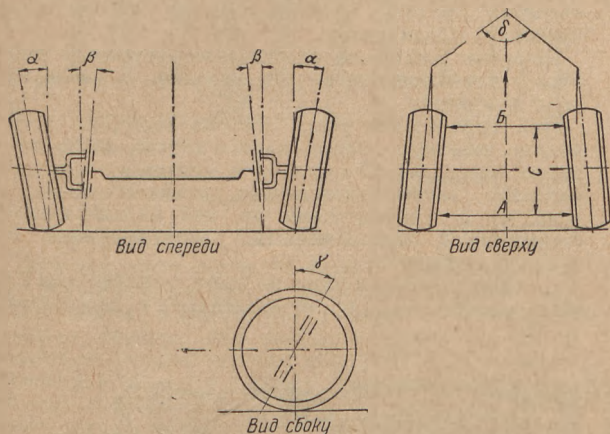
Углы установки передних колес и шкворней автомобиля.
